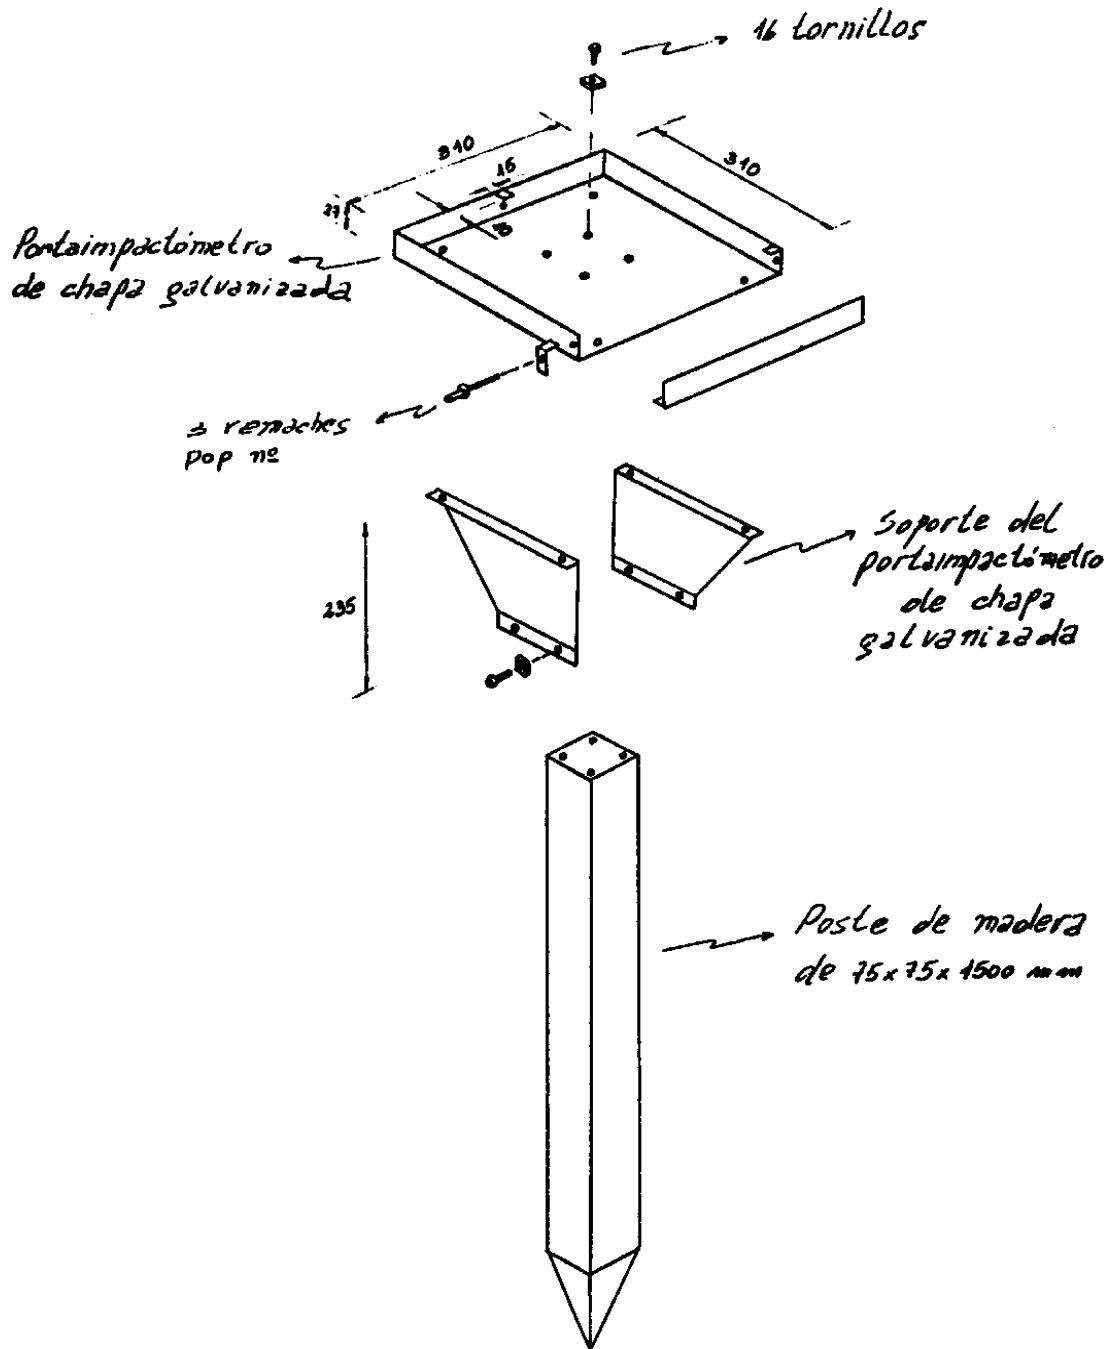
Dibujo del porta placa con detalles para su fabricación.
